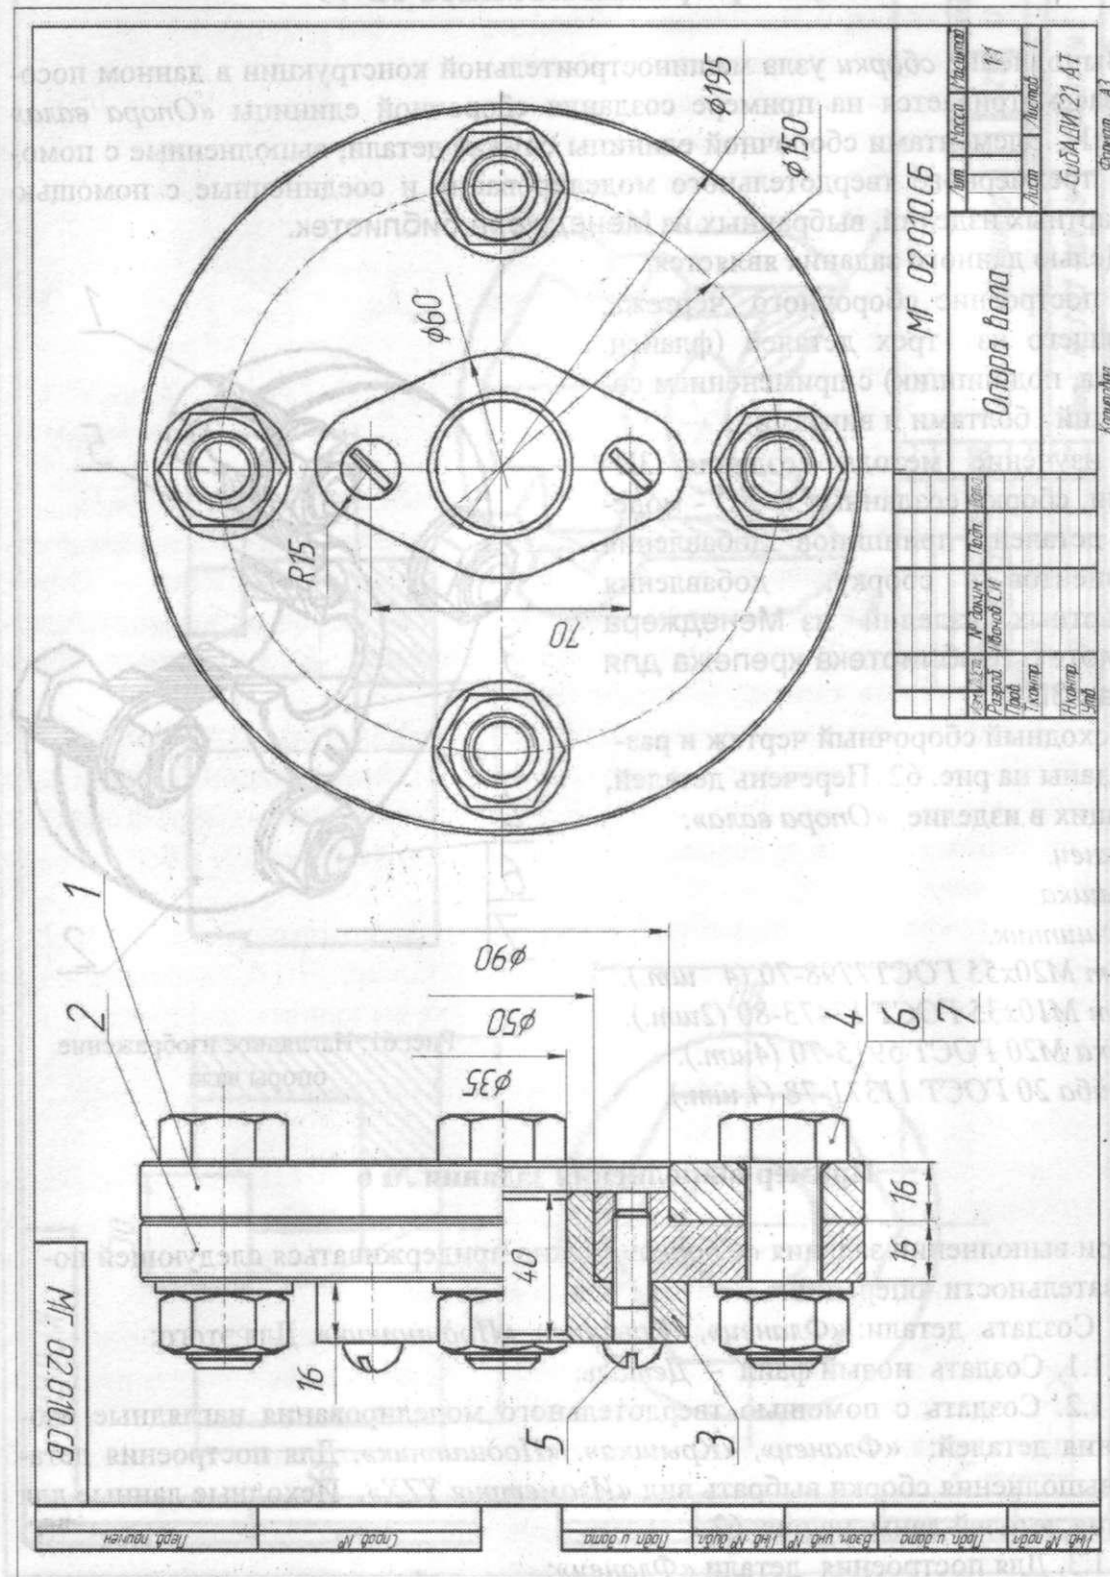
Сборочный чертёж «Опора вала» — исходные данные для выполнения сборки узла машиностроительной конструкции
